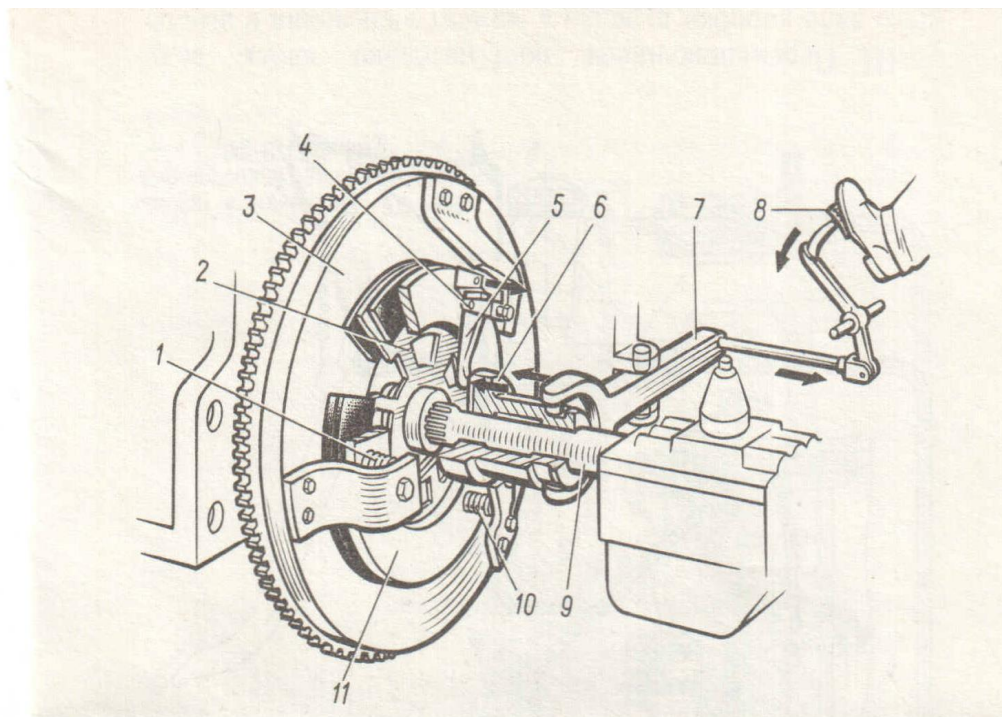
1, 10 - нажимная пружина; 2 - ведомый диск; 3 - маховик; 4 - ось рычажка; 5 - отжимной рычажок; 6 - муфта с выжимным подшипником; 7 - вилка сцепления; 8 - педаль; 9 – вал; 11 - ведущий диск;
